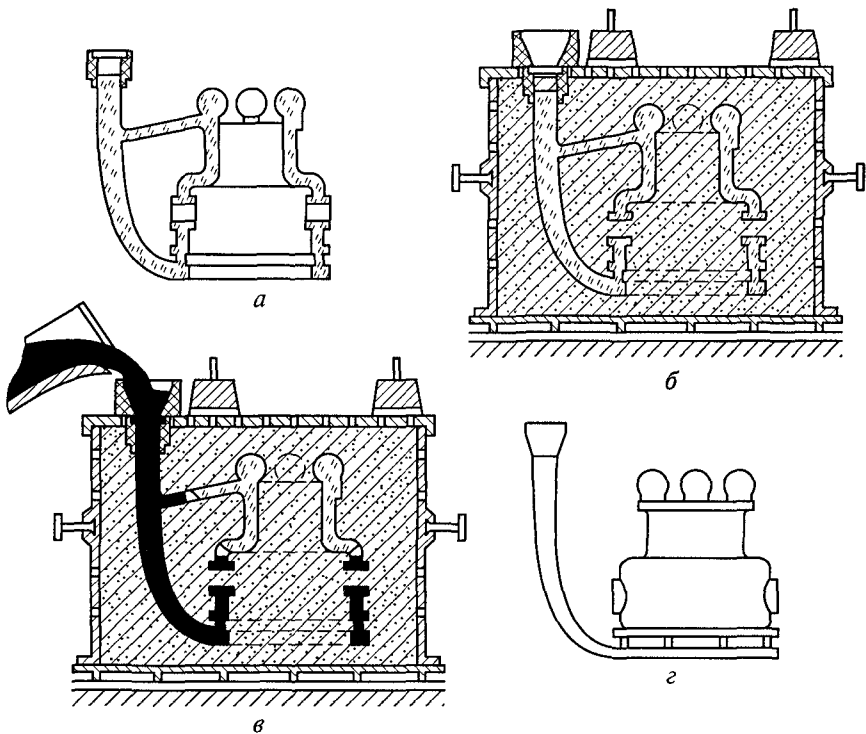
Схема изготовления отливки по газифицируемой модели:
